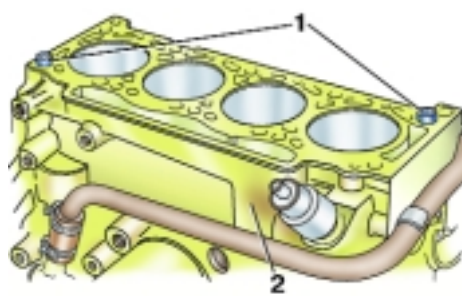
Расположение установочных втулок головки блока двигателя F3R 272: 1 – установочные втулки; 2 – блок цилиндров двигателя
